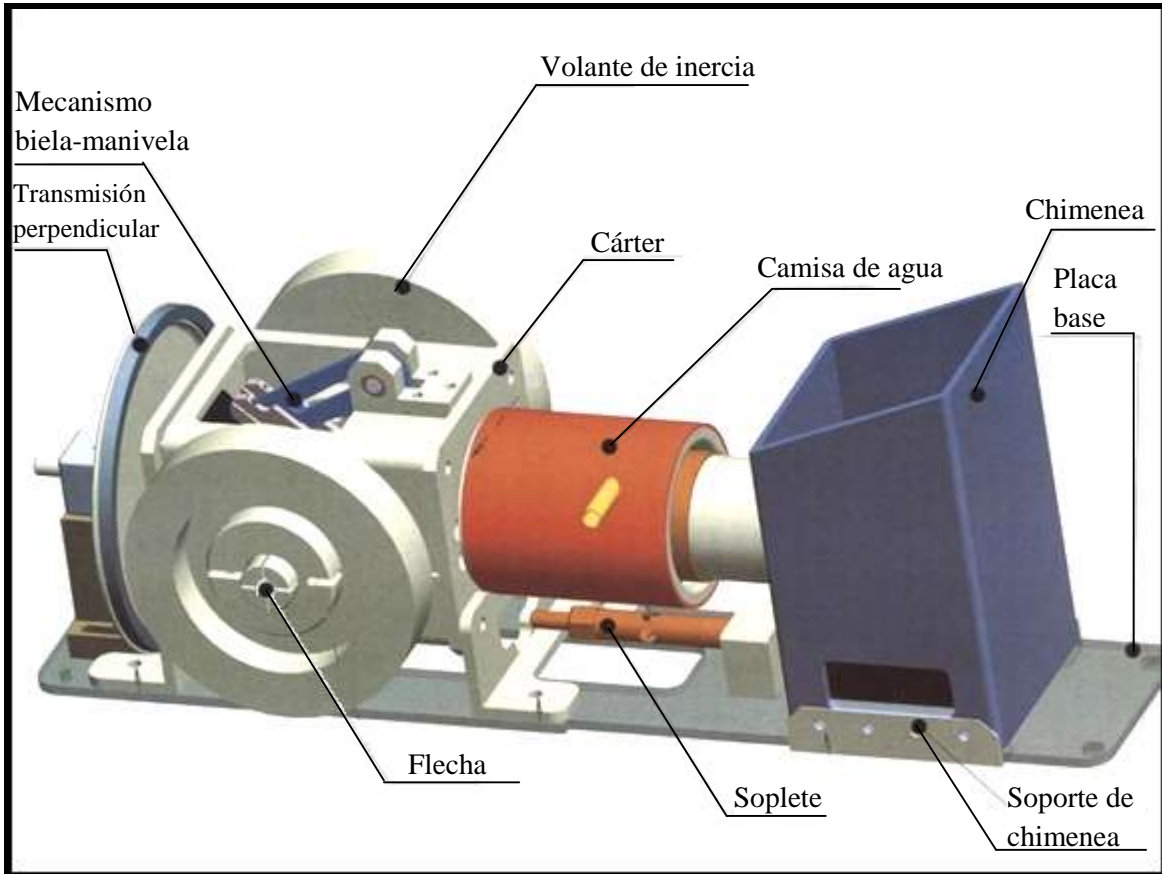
Ensamble general del motor Stirling Silver II. Fuente: [5].
